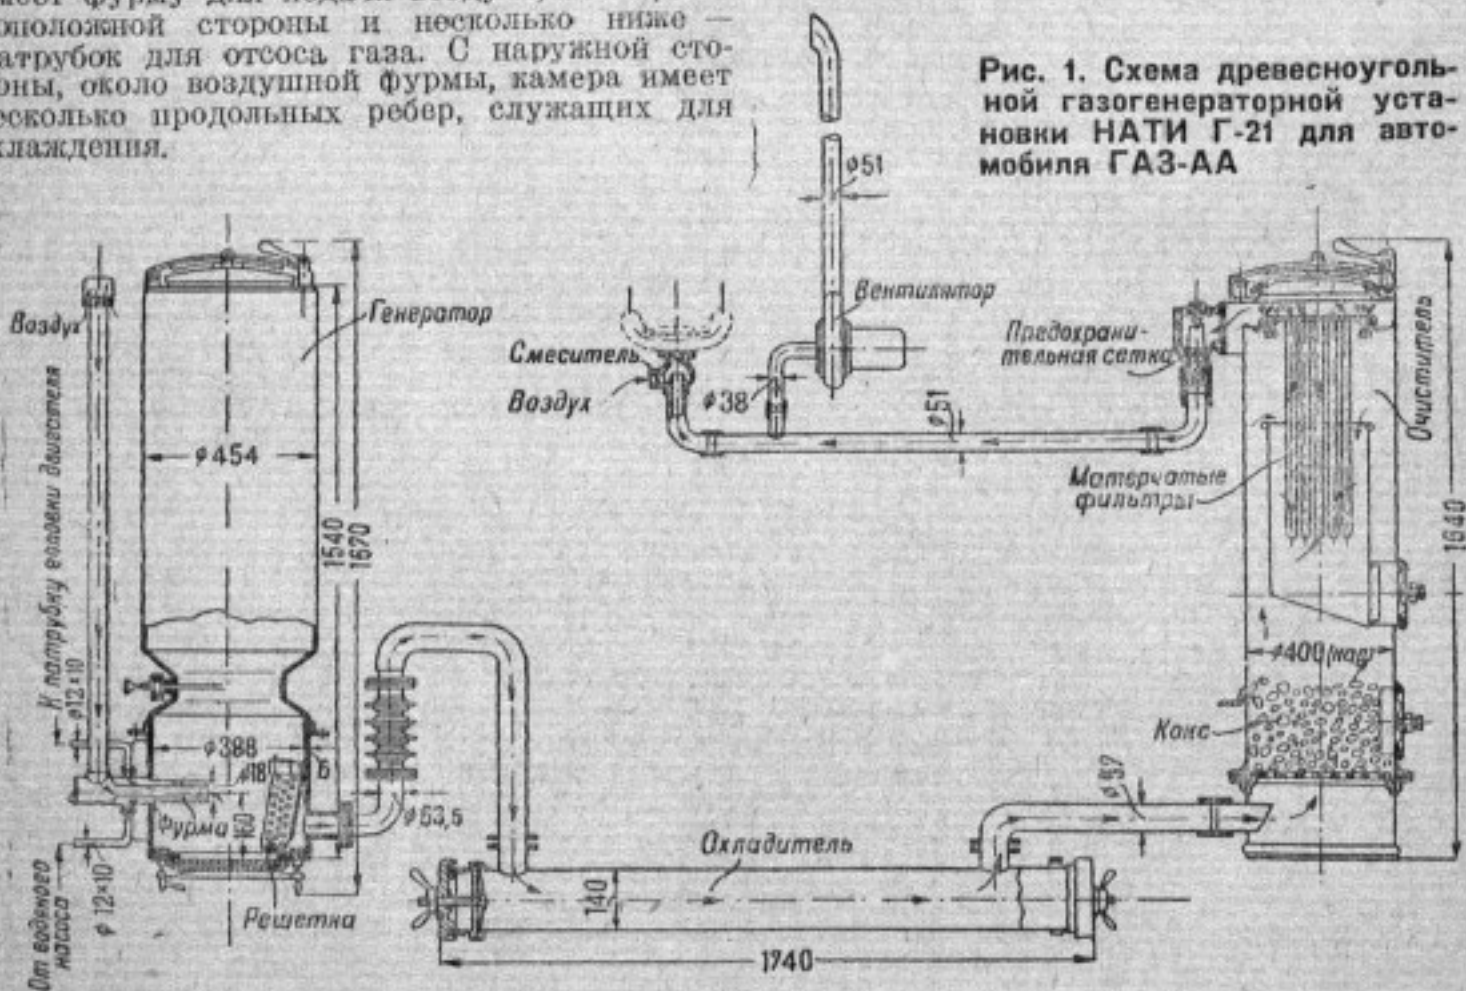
Схема древесноугольной газогенераторной установки НАТИ Г-21 для автомобиля ГАЗ-АА
